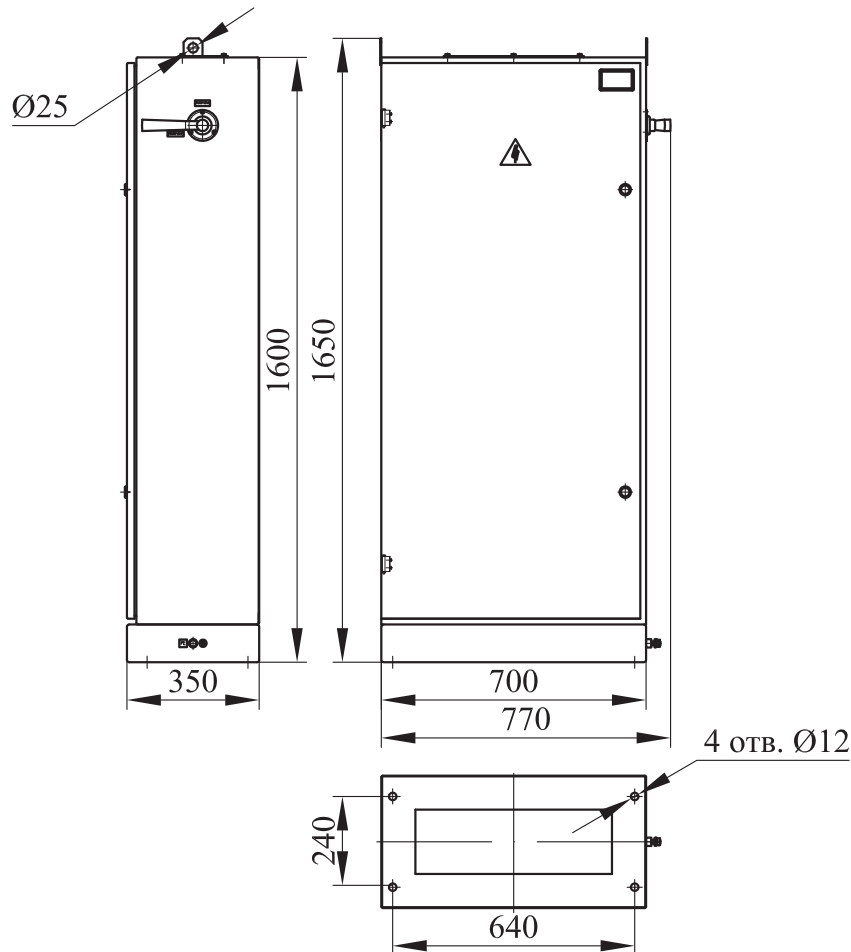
Габаритные и присоединительные размеры шкафов по схеме 01-18
